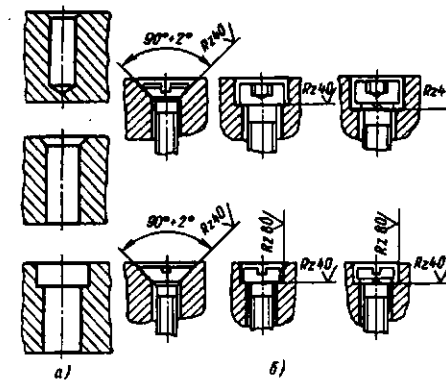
Отверстия под нарезание резьбы и головки винтов, обрабатываемые ступенчатыми сверлами
